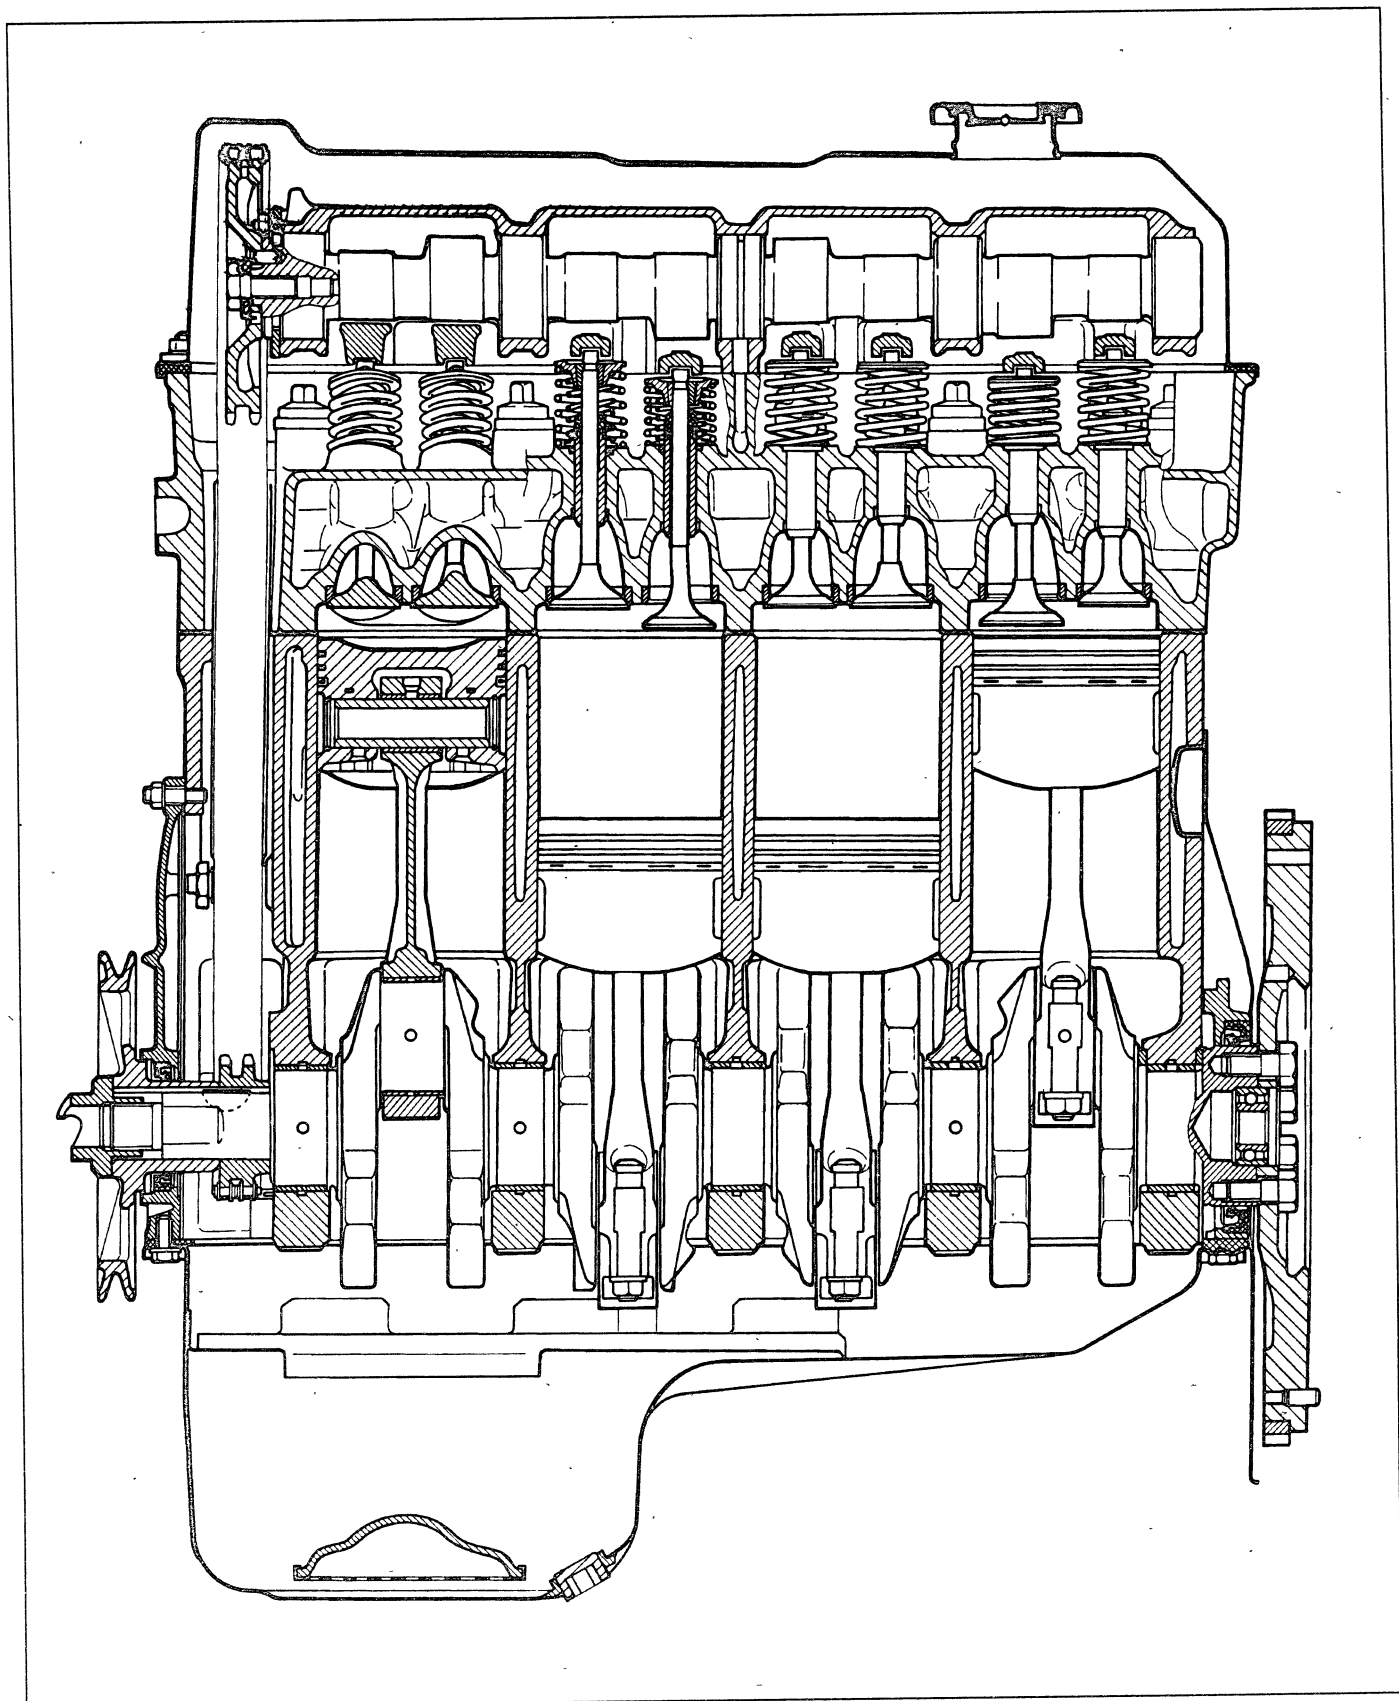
Продольный разрез двигателя ВАЗ-21213
